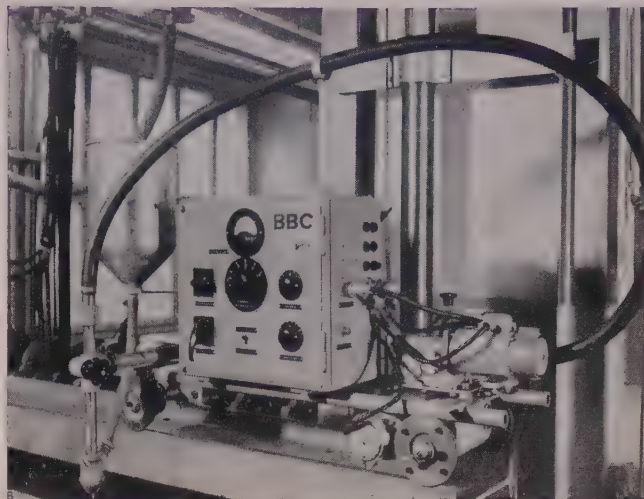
BBC-Lichtbogen-Schweißautomat in fahrbarer Ausführung.
